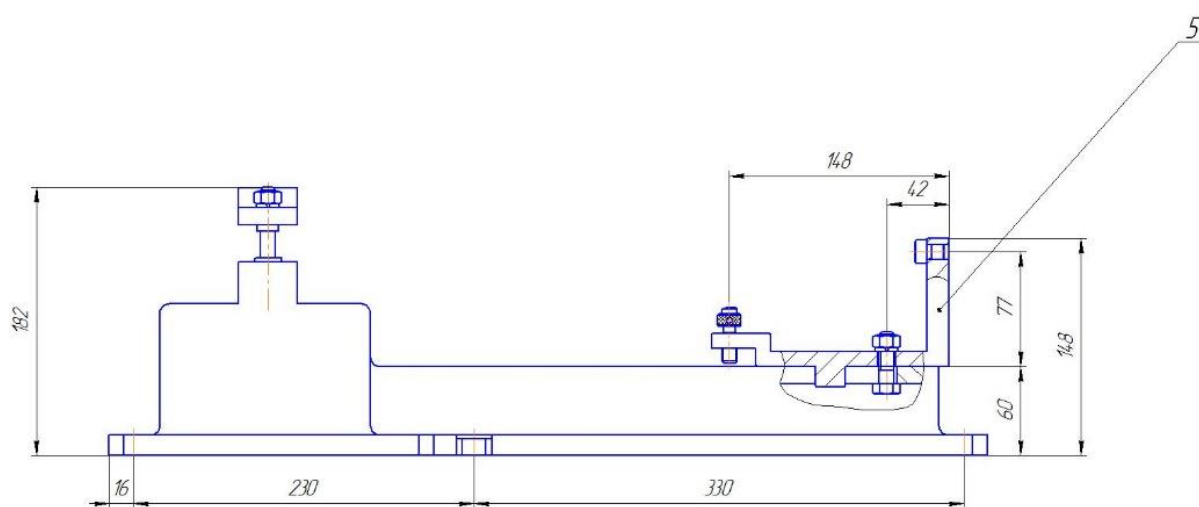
Головний вигляд фрезерного пристосування
